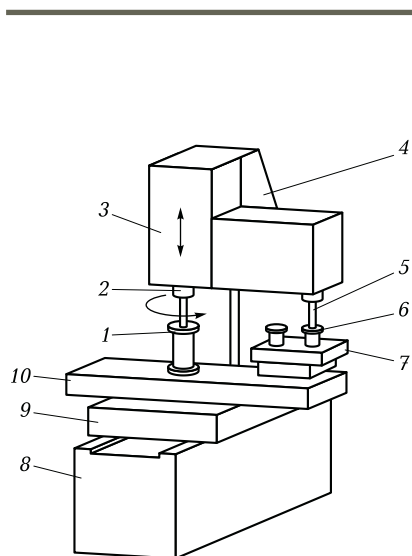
Копировально-фрезерный станок с вертикальным расположением шпинделя и горизонтальной поверхностью стола:
